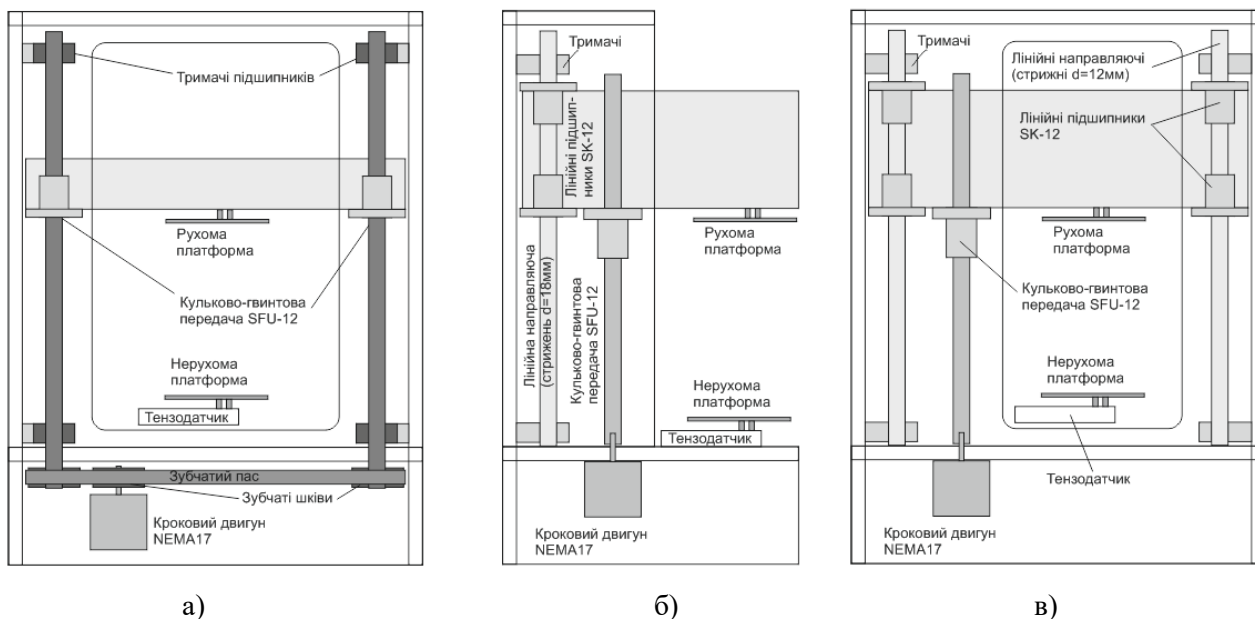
Схеми навантажень випробувальних установок (а – двоколонна, б – консольна, в – змішана)
